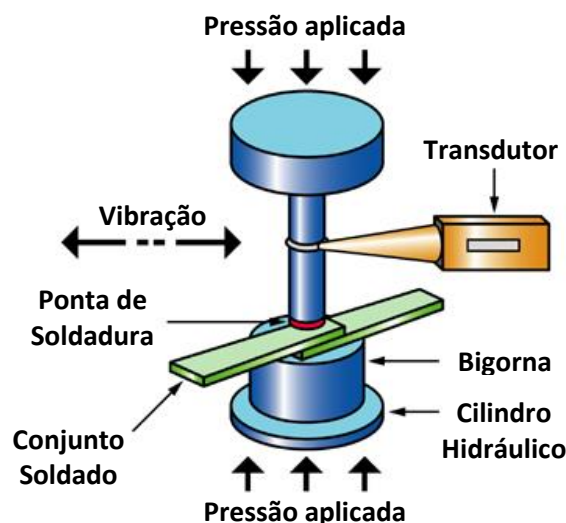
Representação Simplificada do Processo de Soldadura por Ultrassons (adaptado de [41]).
